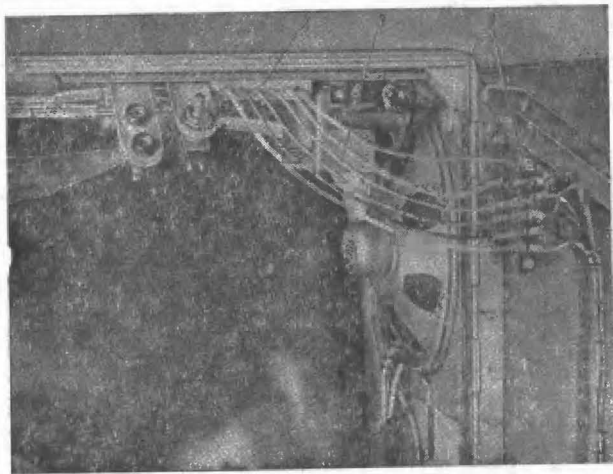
Верхняя монтажная планка правой створки. 1 — монтажная планка; 2 — деревянный брусок; 3 — провод.
